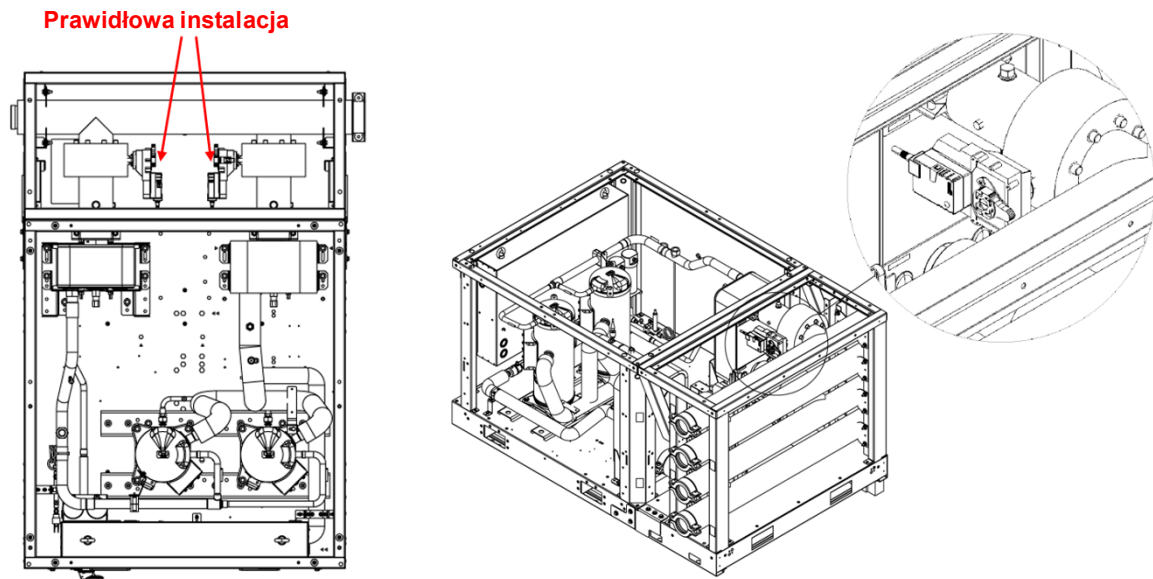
Instrukcje montażu wyłączników krańcowych silownika
